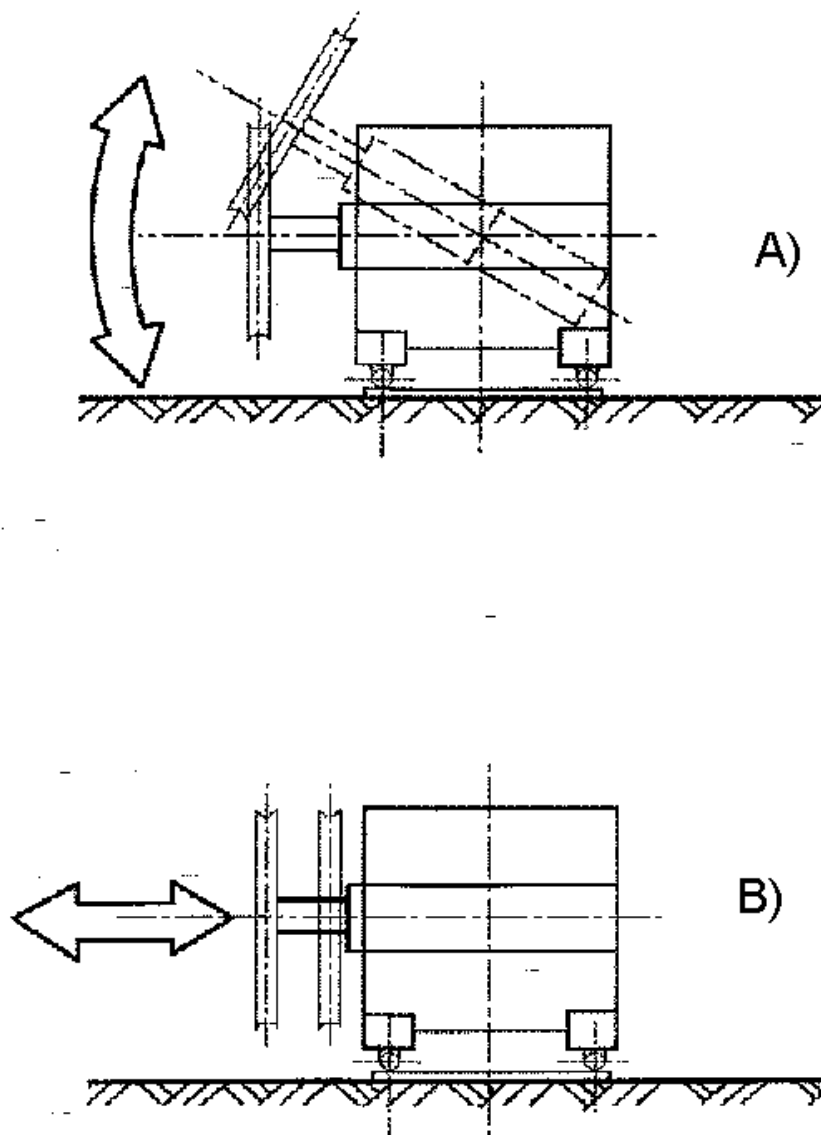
Схемы регулировки положения каната относительно уступа и канатной установки: поворотом шкива (А) и поперечным перемещением шкива (В).
